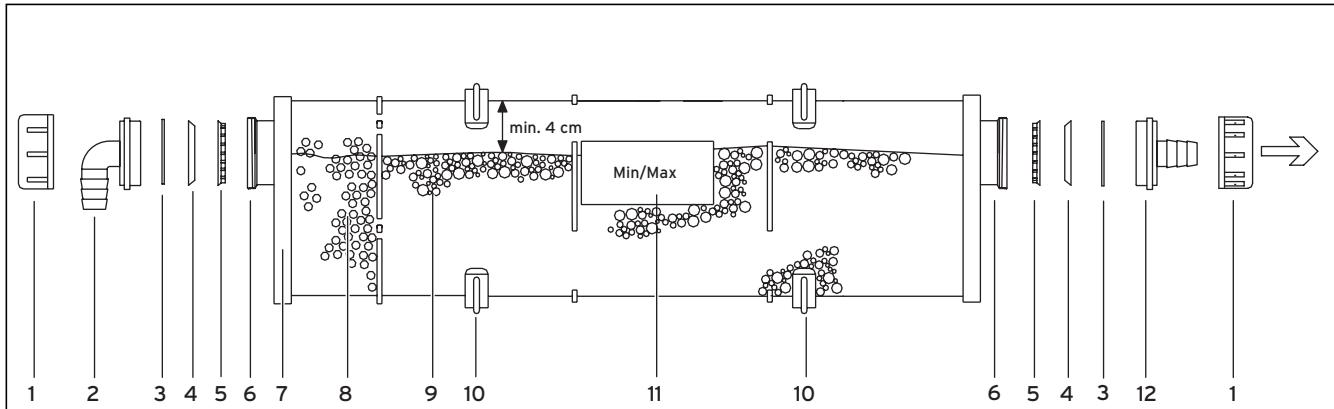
Construction du dispositif de neutralisation du mazout
